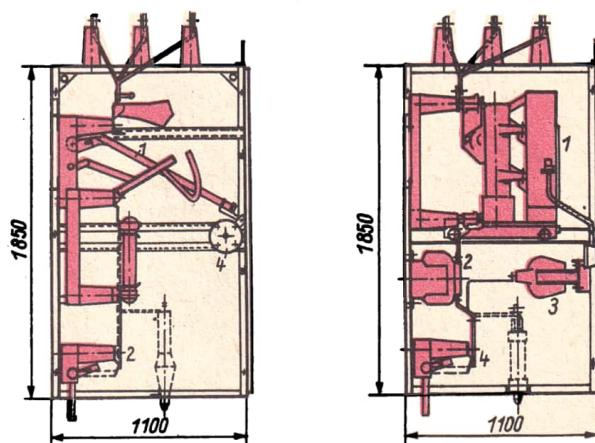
Einfachschaltzelle BSI mit festeingebautem Lasttrenner
